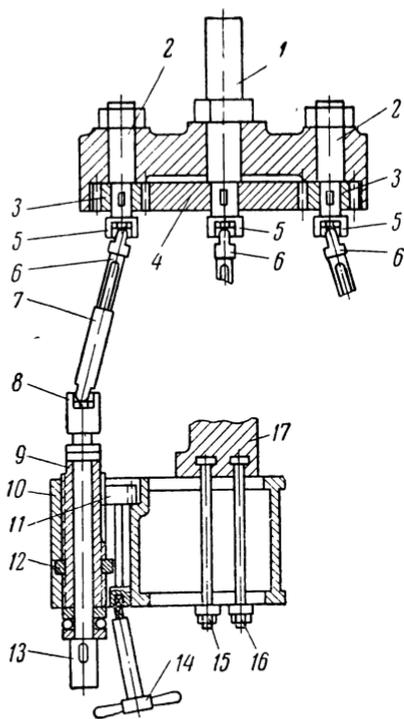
Многошпиндельный сверлильный станок с переставными шпинделями
